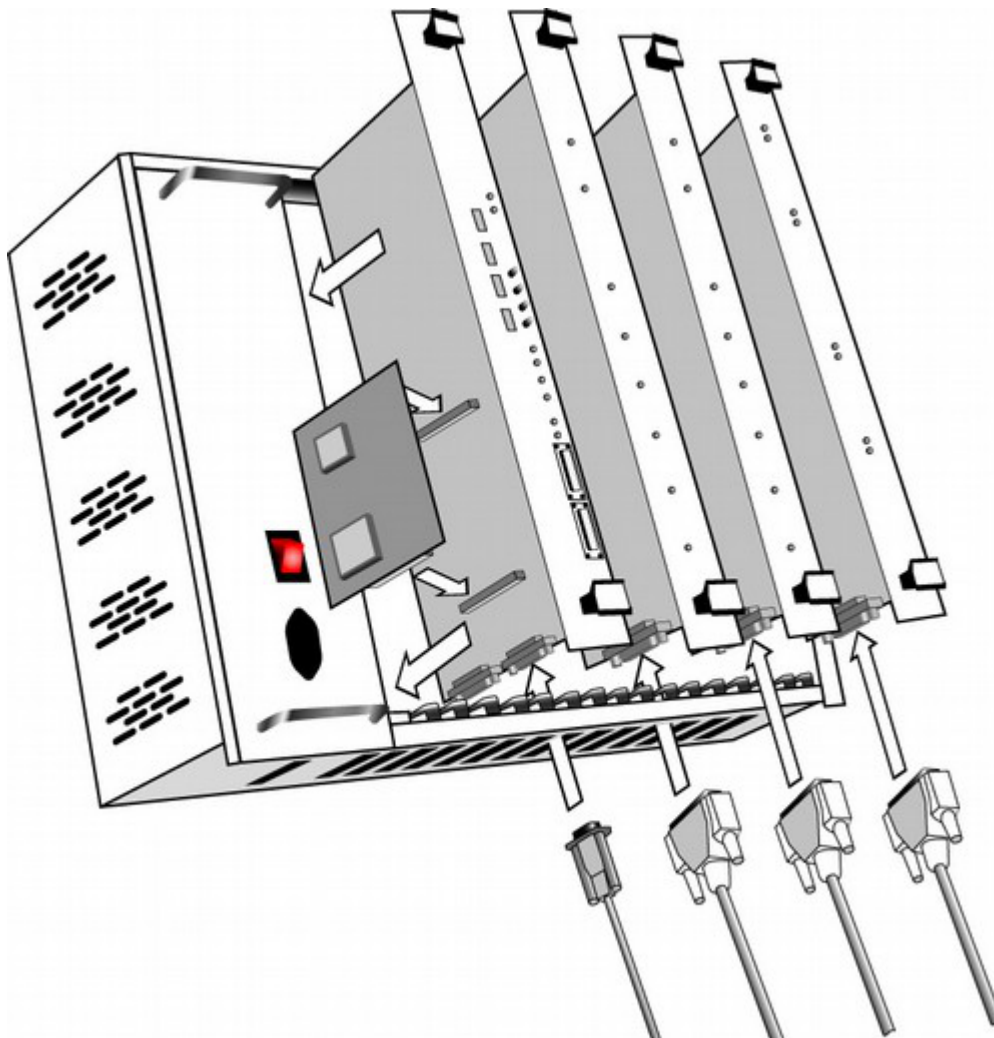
Внешний вид корпуса ЦАТС, установка ЭМ и подключение кабелей
